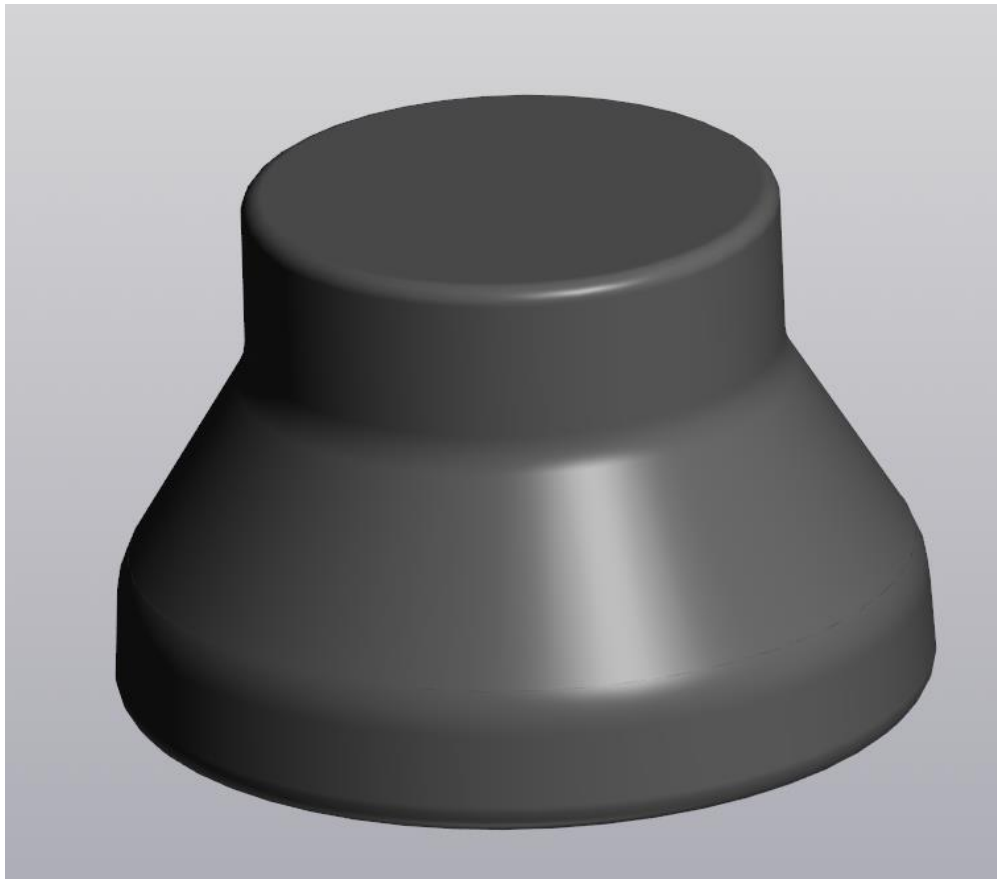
3D модель заготовки для визначення маси штамповки
